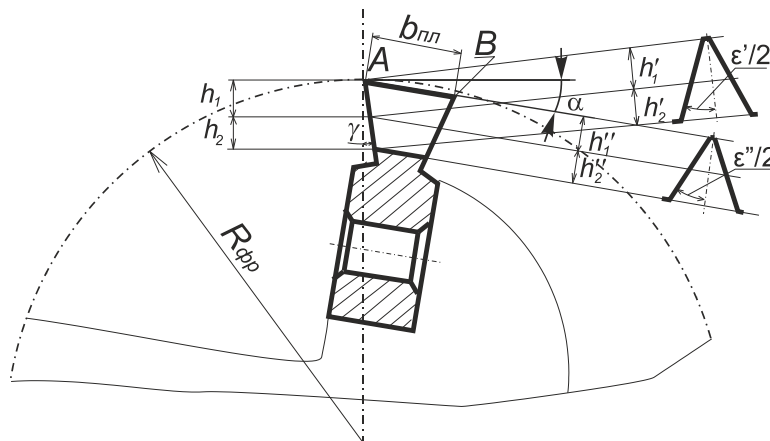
Схема встановлення твердосплавної непереточуваної пластинки у корпусі гребінчастої фрези
